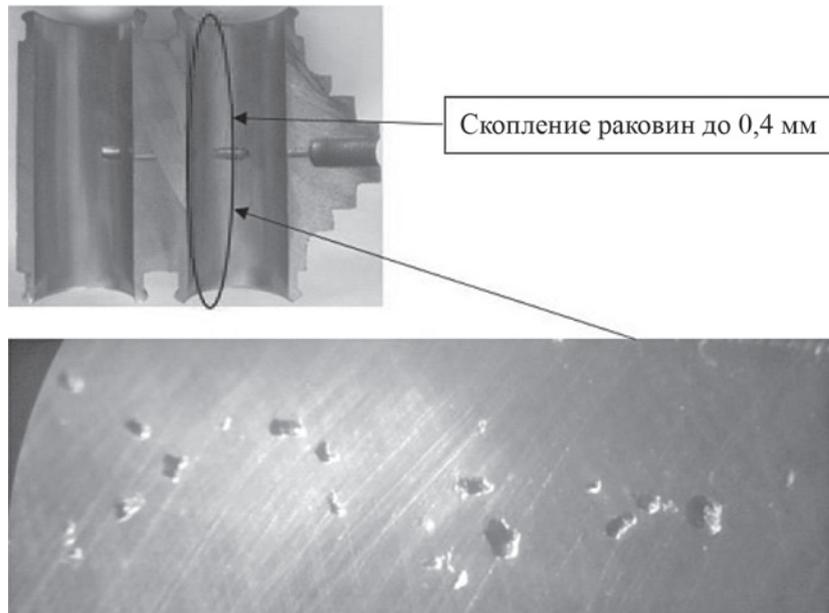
Фото дефекта «подкорковая раковина» отливки «Цилиндр Колесный»
